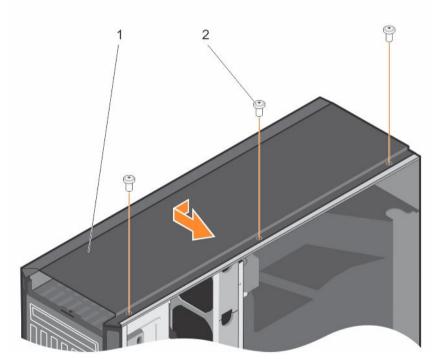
Extracción de la instalación de la cubierta superior del sistema
